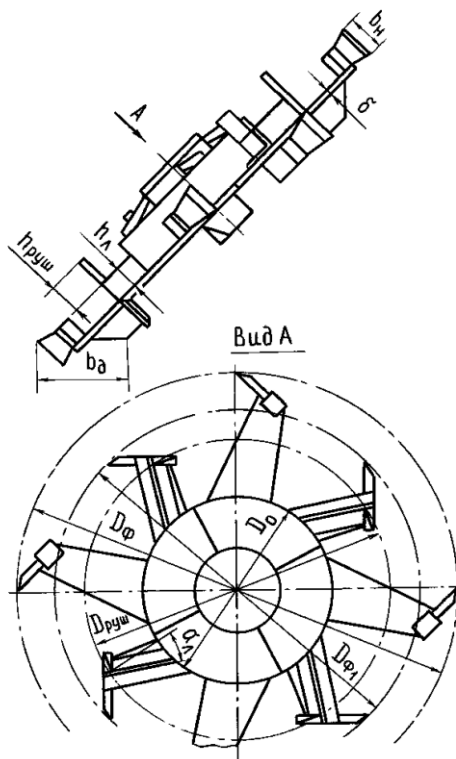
Фреза плужно-фрезерного каналопателя
